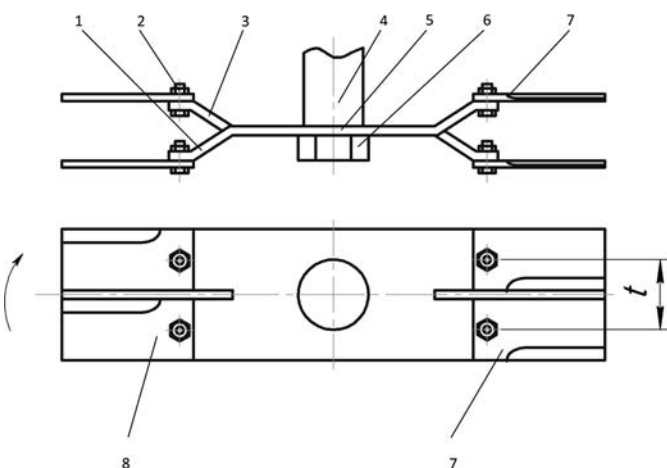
Двоярусний різальний апарат з послідовною роботою ножів: 1 – смуга нижнього ярусу; 2 – вісь закріплення ножа; 3 – смуга верхнього ярусу; 4 – привідний вал; 5 – тримач; 6 – притискний болт; 7 – ніж верхнього ярусу; 8 – ніж нижнього ярусу
